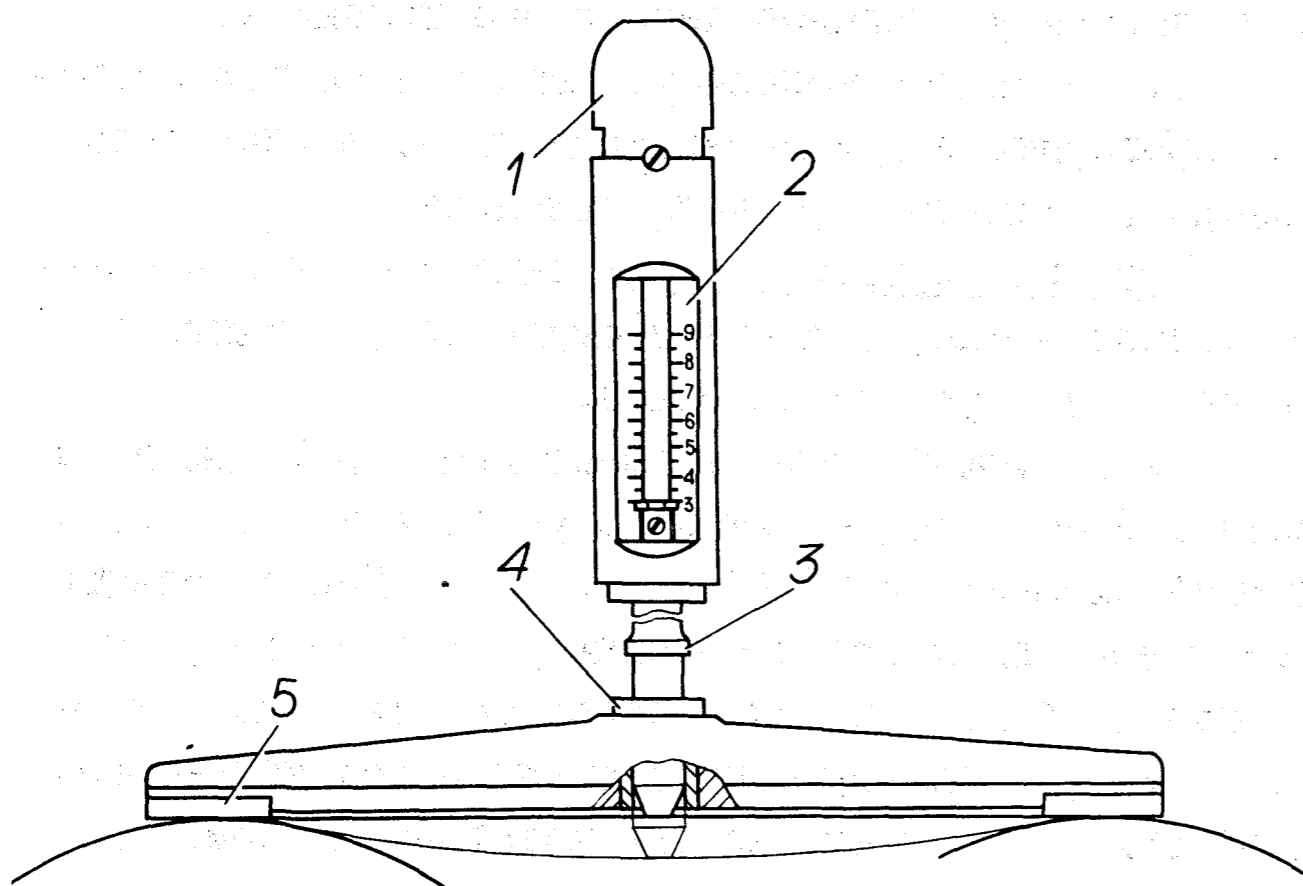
Динамометр 7870-8679 для проверки натяжения ремня привода вентилятора: I - ручка; 2 - шкала; 3 - бурт; 4 - втулка; 5 - планка
